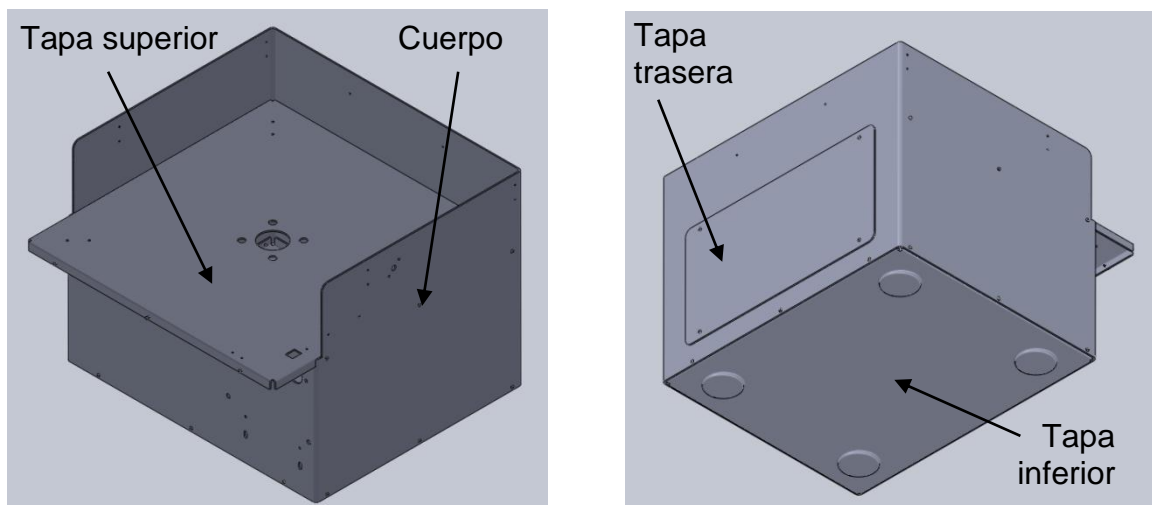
Estructura de soporte – Plano ref. PI-104-00-00
